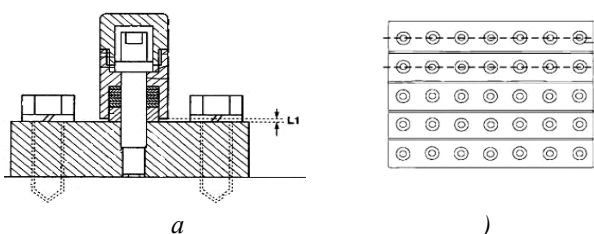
Штыревой амортизатор, несущая пластина, нагружаемое устройство, штамповая подушка, прессовое оборудование и метод прессования: а – общий вид упругого узла; б – расположение элементов в матричном поле
